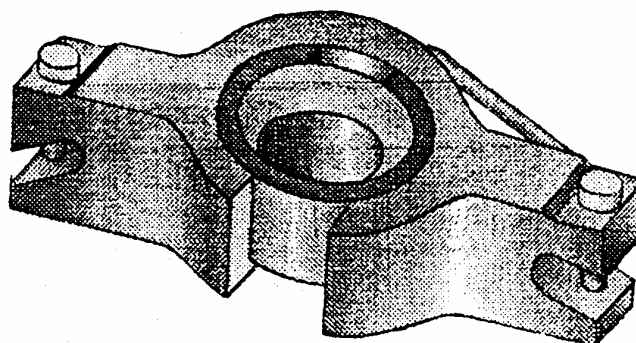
Двухштропный элеватор типа ЭХЛ
